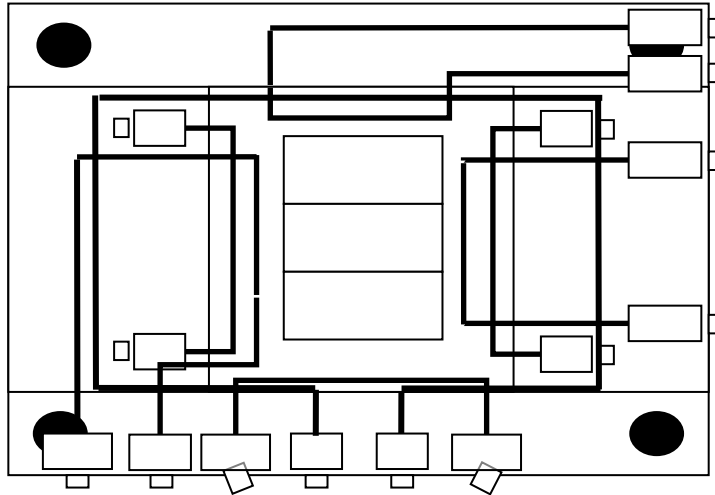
Komora stykače s vtokovou soustavou – zaformování.
